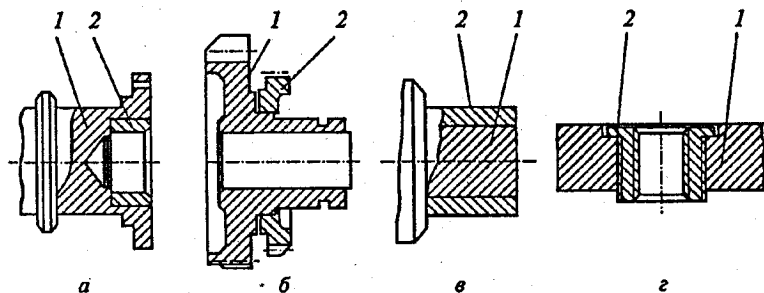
Восстановление изношенных отверстий (а), шестерен (б), шеек цапф (в), резьб (г) постановкой дополнительных деталей:
